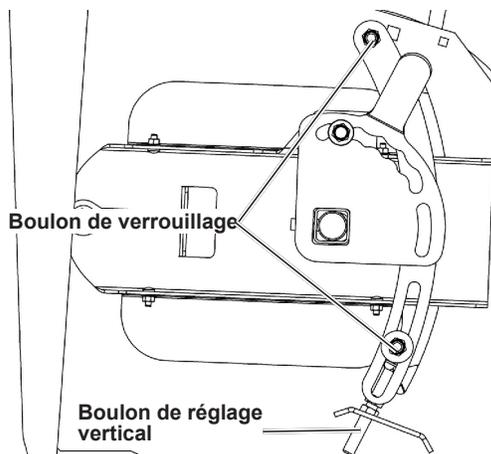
Réglage de la hauteur du tambour de la vis sans fin
